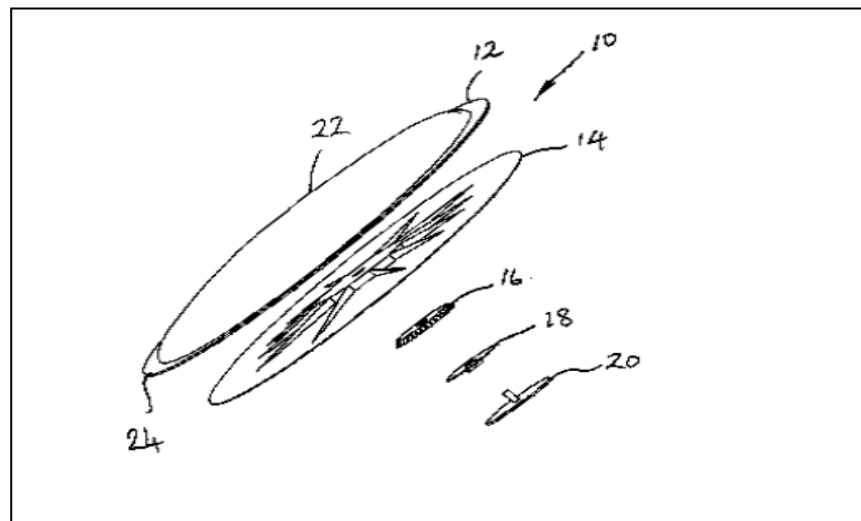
Vista en perspectiva del despiece ordenado de una cubierta de acceso al depósito de combustible. Fuente: EP2492200.
